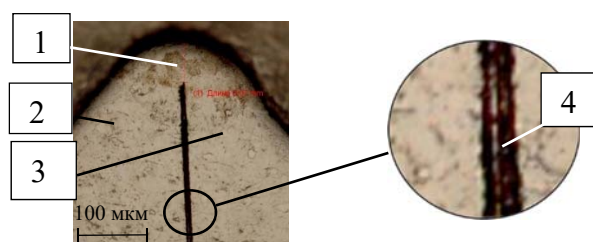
макроструктура сварного шва 1 – сварной шов, 2 – шайба, 3 – корпус, 4 – окно (фольга толщиной 0,003 мм)
